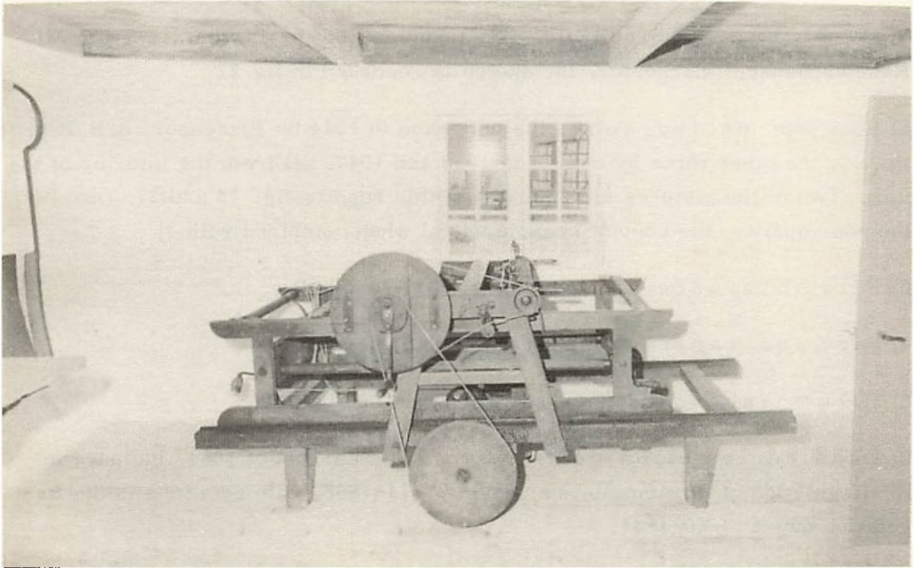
neg. 1768.37: 08-05-65: Ruemaskine. Roughing machine.
